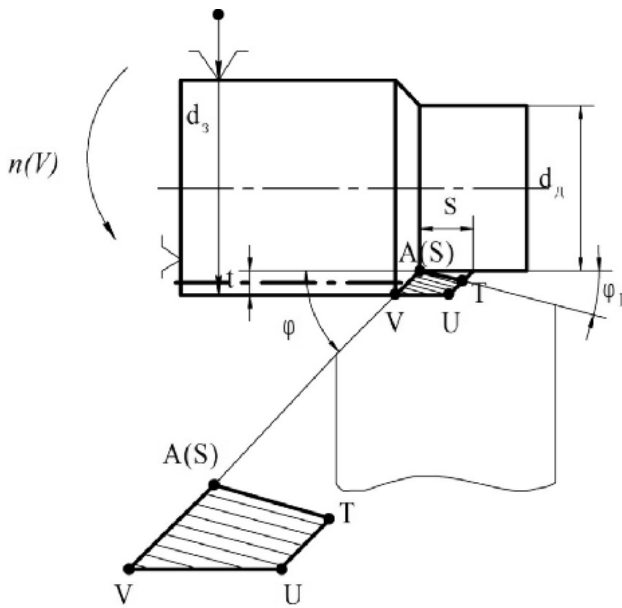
Схема первоначального контакта вершины резца с обрабатываемой поверхностью заготовки
